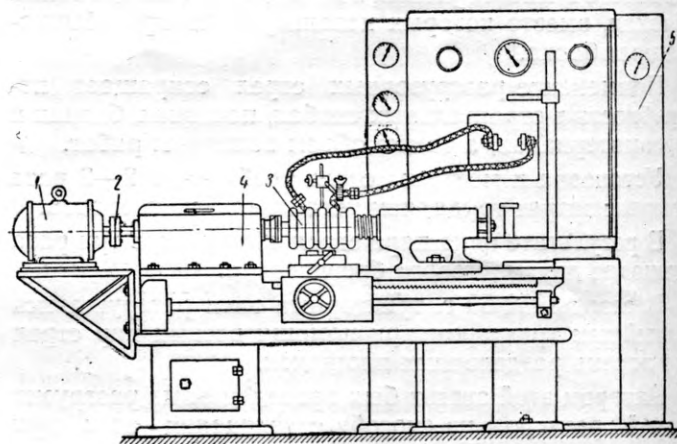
Установка для центробежной заливки вкладышей и втулок:
